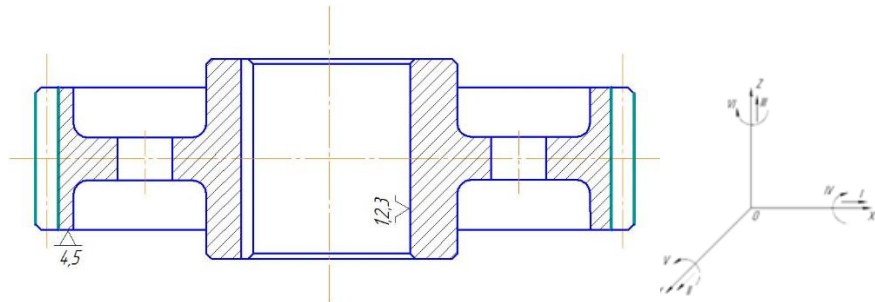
Схема базування заготовки при зубонарізанні
